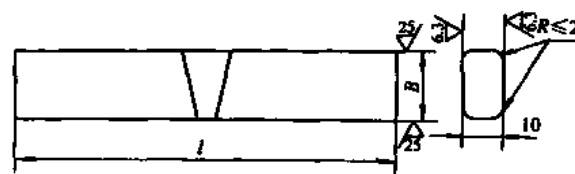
焊接接头侧向弯曲试样形状和尺寸
